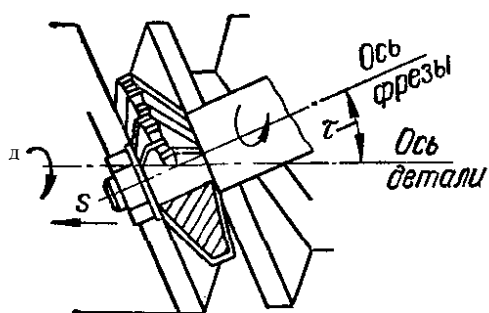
Схема нарезания резьбы дисковой фрезой
